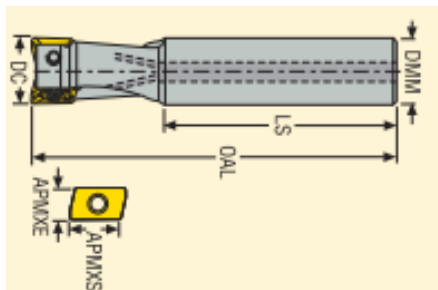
Фреза R217.69-1820.0-06-4AN [З с. 24]
